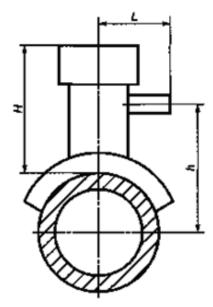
Размеры седловых деталей с закладными электронагревателями раструбных концов деталей: h — высота бокового отводного патрубка (расстояние между осью трубы и осью отводного патрубка); L — длина вылета бокового отводного патрубка (расстояние между осью трубы и торцом отводного патрубка); H — максимальная высота седлового отводна
